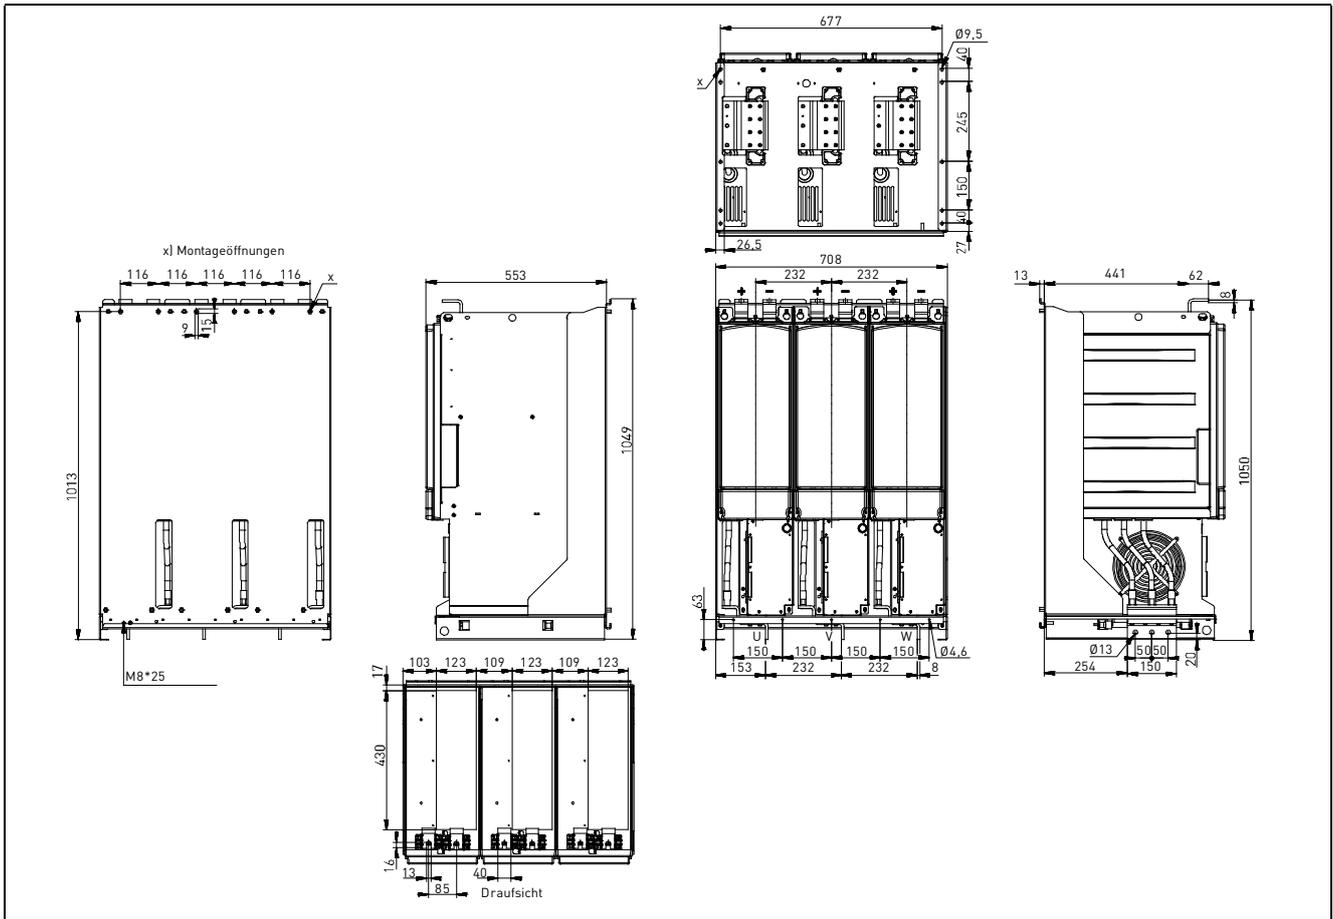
Maßzeichnung – Umrichtermodul (Baugrößen FR13/14)
